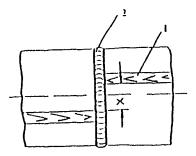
2. Схема сварки труб с продольным швом: 1 - продольный шов; 2 - кольцевой шов; X - не менее 100 мм
